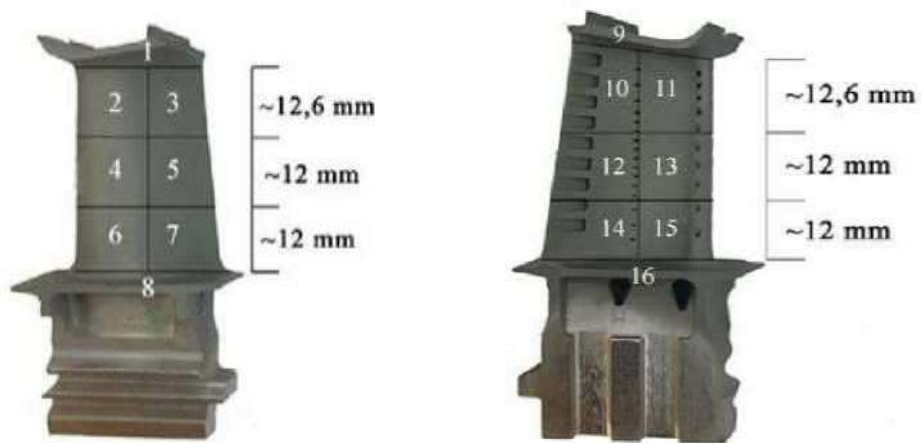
Робоча лопатка з типовою розміткою на зони
